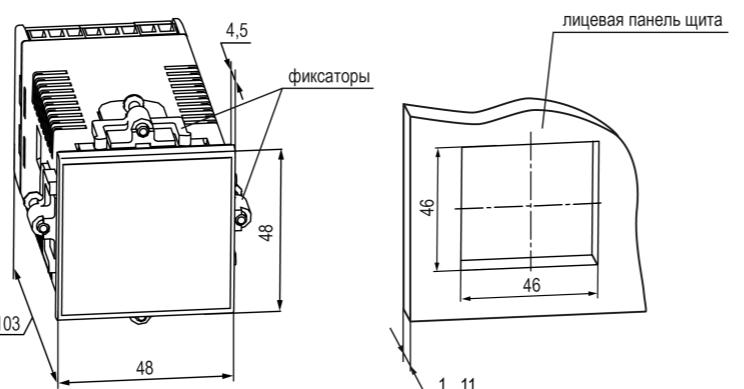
Габаритные размеры корпуса Щ5 и монтажного отверстия в щите
